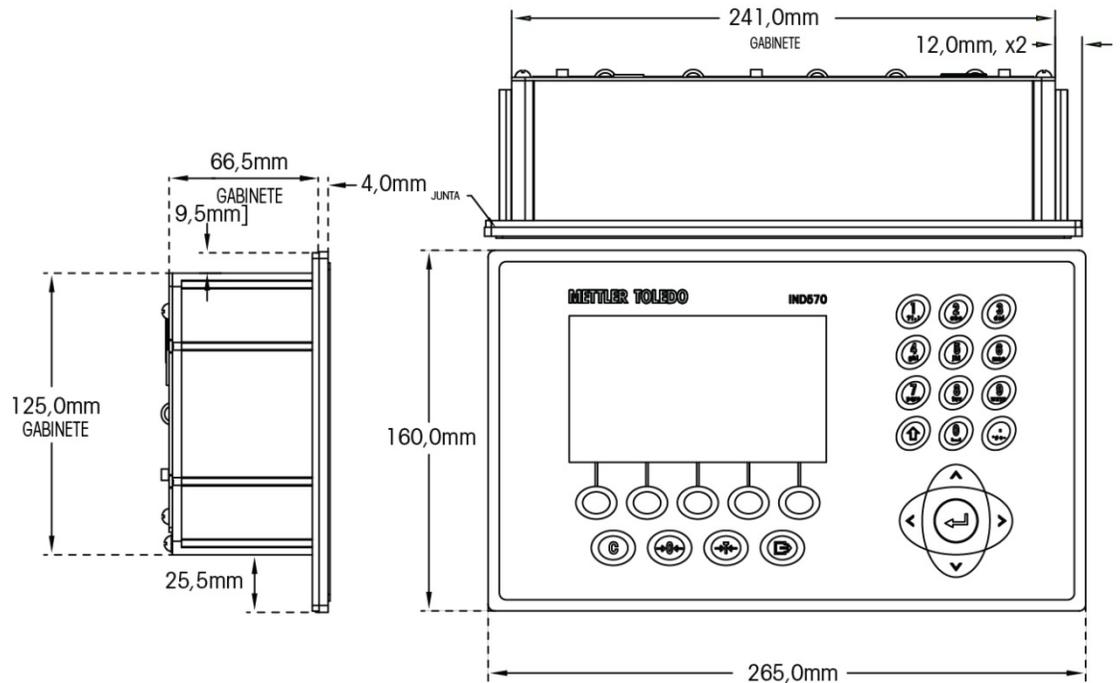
Dimensões do Gabinete do IND570 para Montagem em Painel
